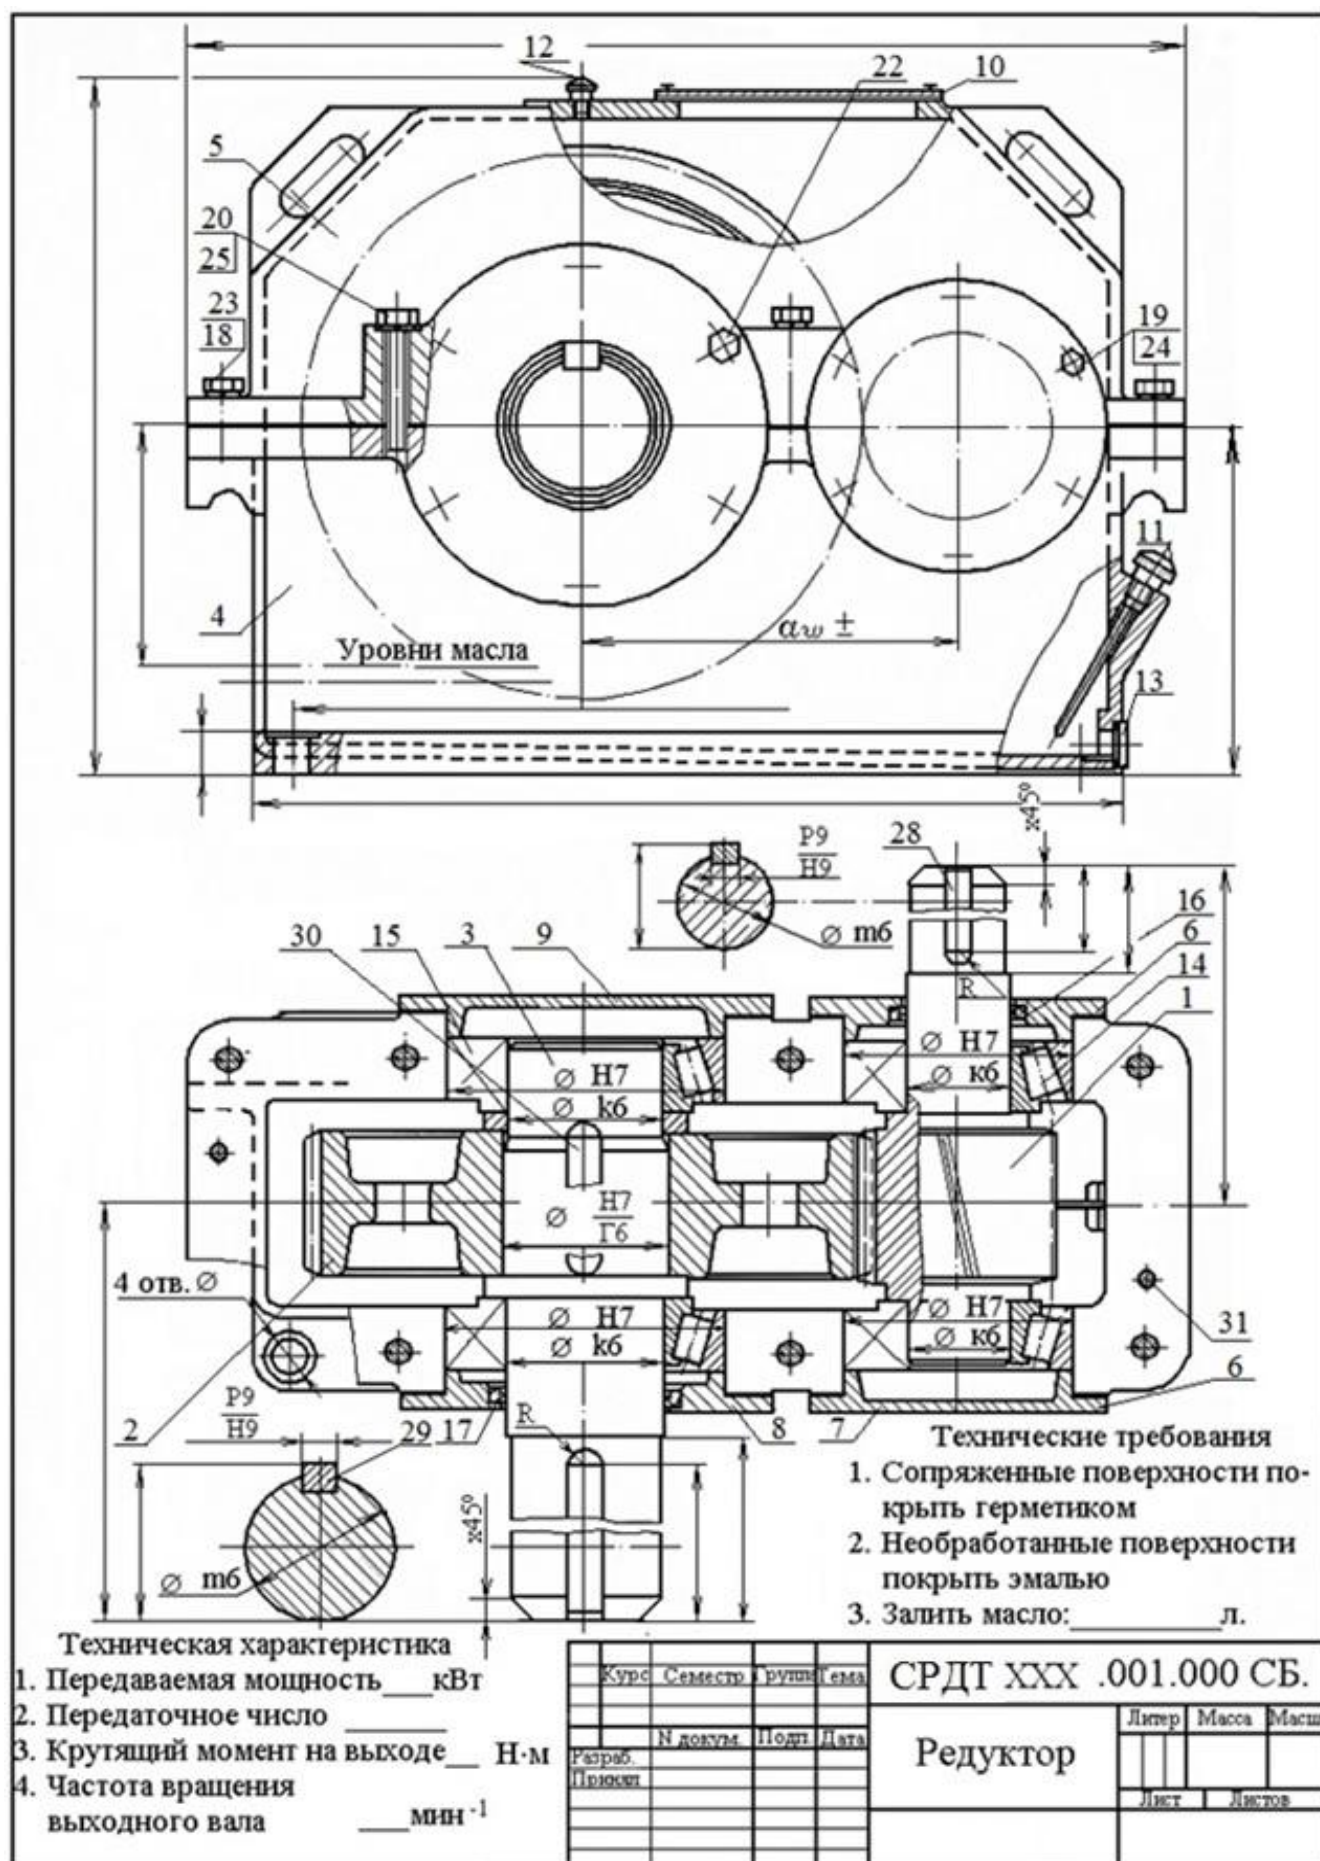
Редуктор цилиндрический одноступенчатый
